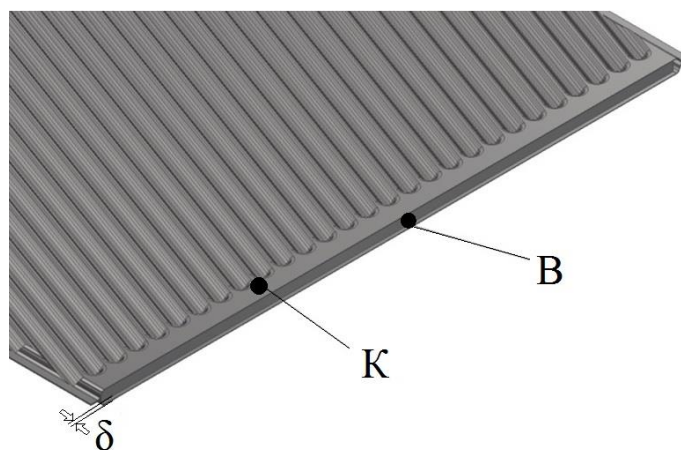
Параметрическая 3D модель технологической вставки для сварки конвертов теплообменника в матрицу: К – конверт; В – вставка; δ – технологический выступ
